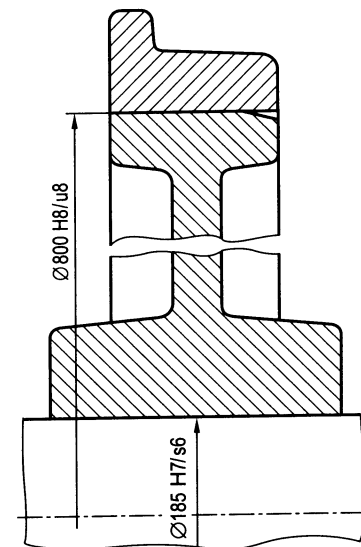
Крепление банджа на центре колеса и центра колеса на валу
